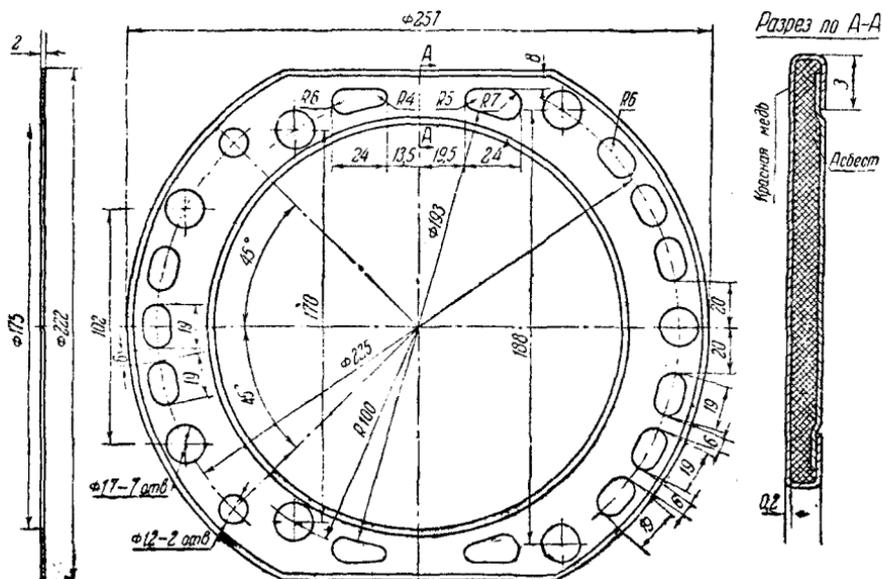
Дет. № 4067. Прокладка головки цилиндра
